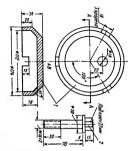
Приспособление для проверки зазора в роликовых подшининках: 1— чашка, 2— винт.
